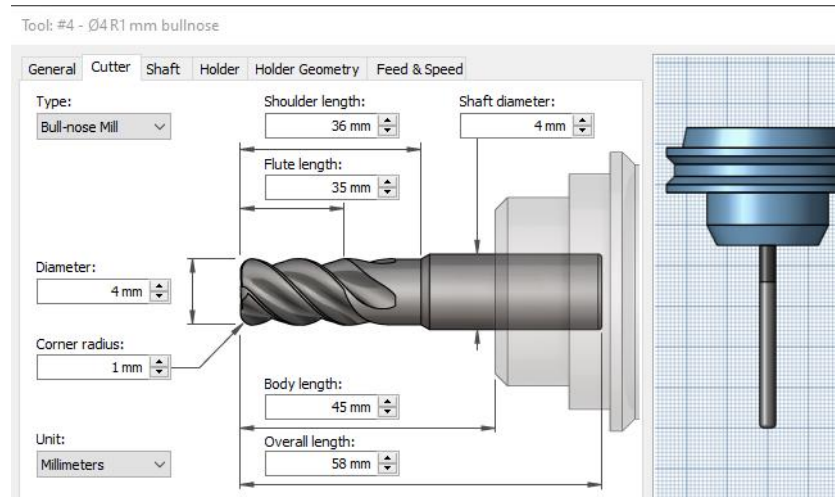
Обираємо фрезу для оброблення отворів
